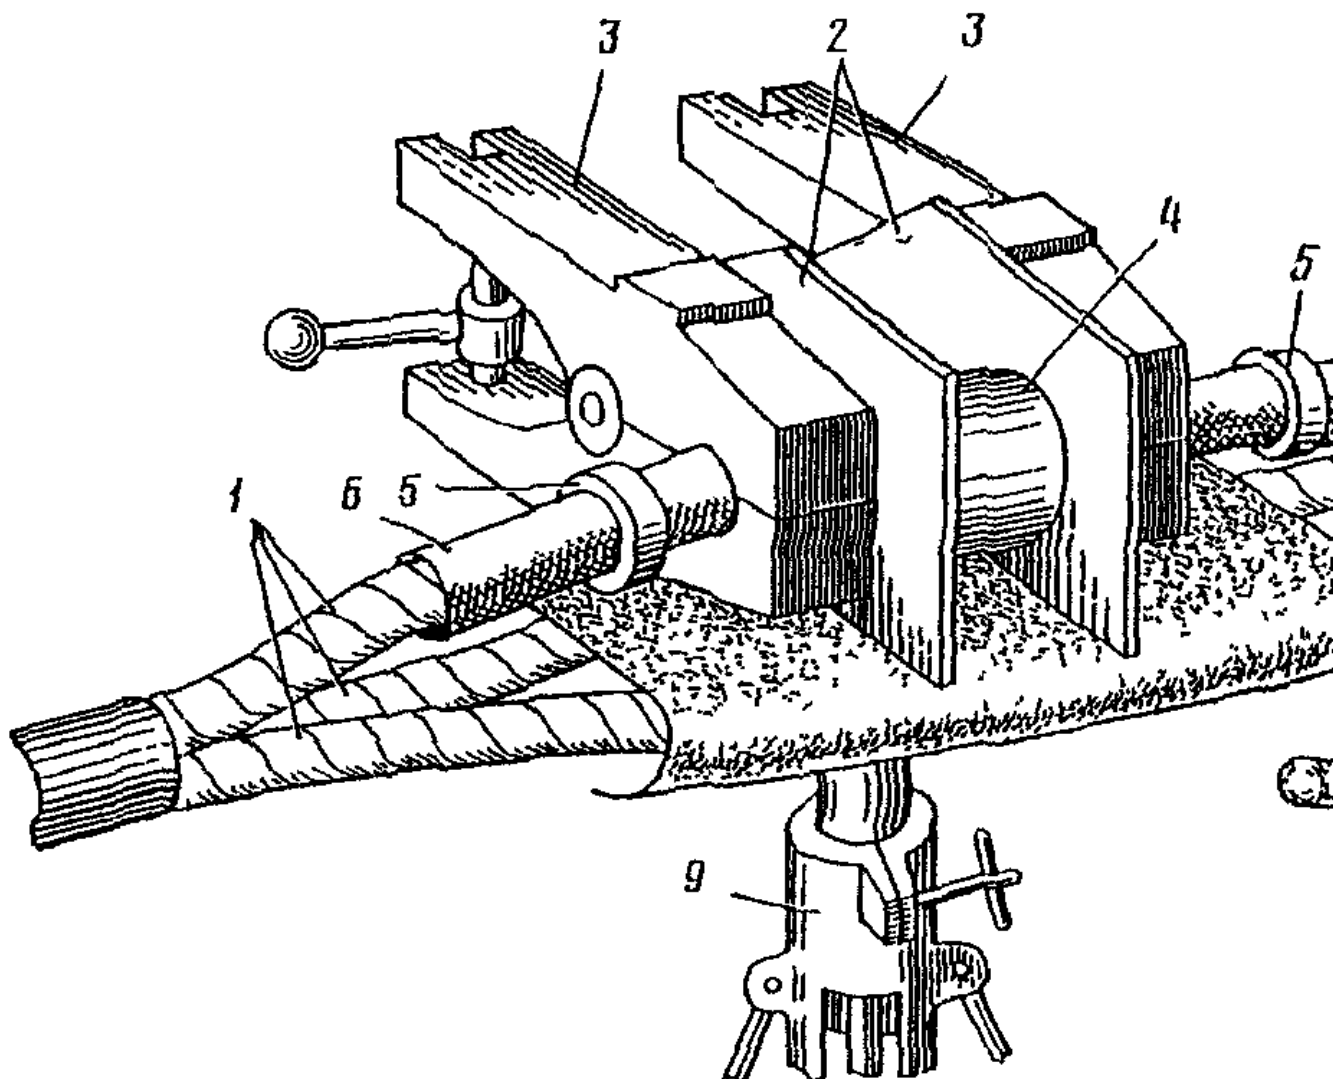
Соединение алюминиевых жил термитной сваркой: 1 - жилы кабеля; 2 - асбестовые экраны; 3 - охладители; 4 - термитный патрон; 5 - зажим крепления поливинилхлоридной трубки; 6 - поливинилхлоридная трубка; 7 - листовый асбест; 8 - термитная спичка; 9 - штатив
